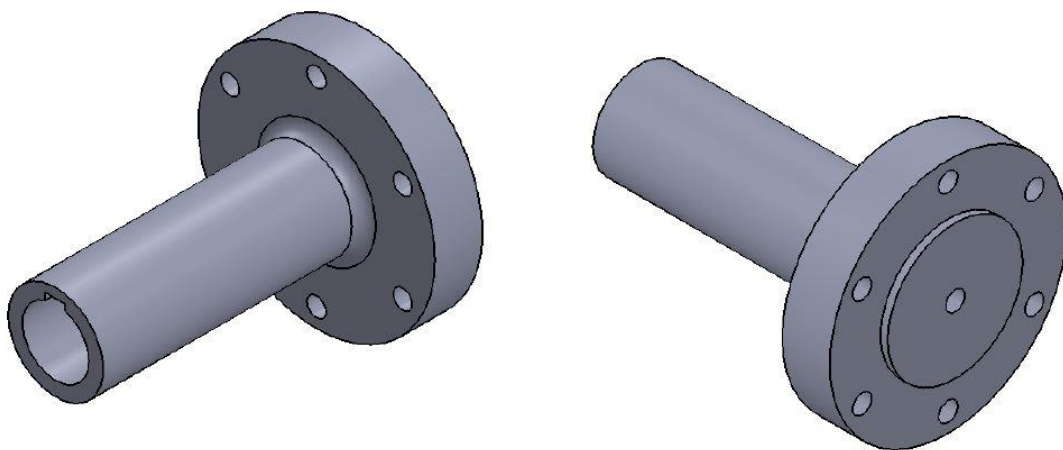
Unión eje motor y junta Kardan. Fuente: Manuel Ángel Ruiz Vilches
